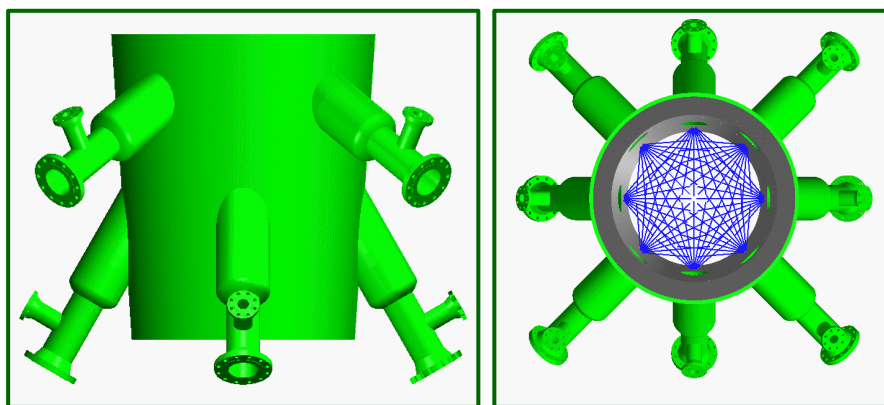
Vistas em elevação e planta dos dispersores *UltraMist*[®]
